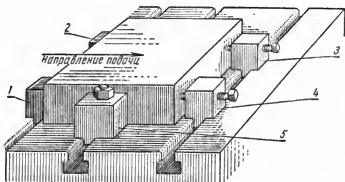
Крепление заготовки на столе поперечно-строгального станка:
